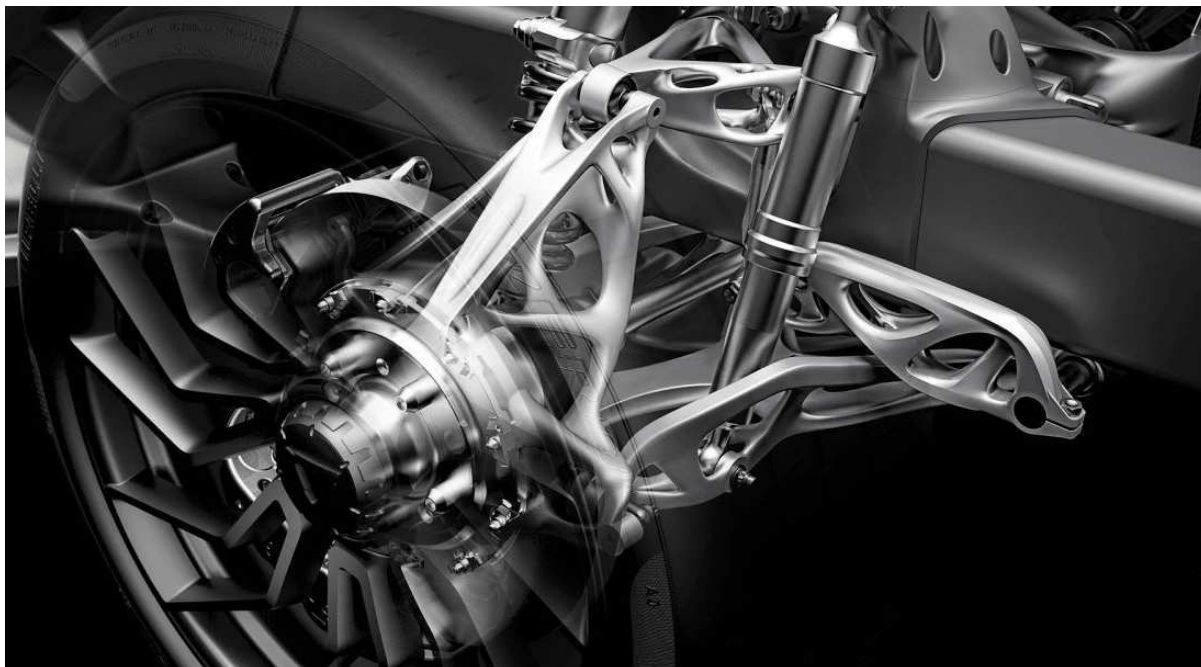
Schematické zobrazenie lichobežníkového zavesenia typu „pull rod“ a „push rod“ [2].
